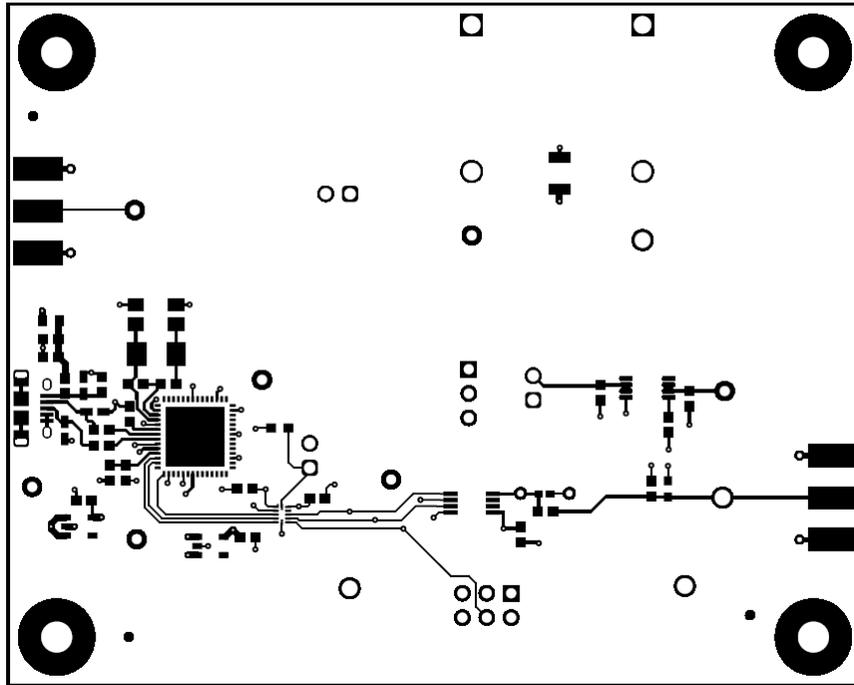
DAC121S101SEPEVM PCB 顶层布局
